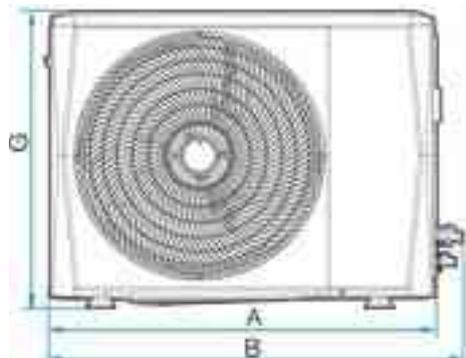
Dimensões da vista superior do modelo 80 (unidade: mm)
